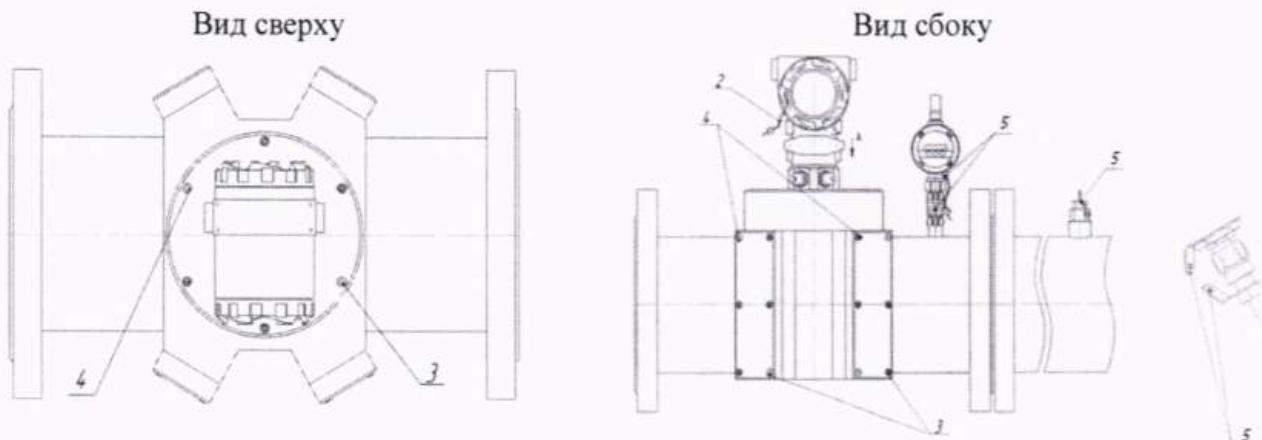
Корпус круглого сечения с раздельными защитными крышками
